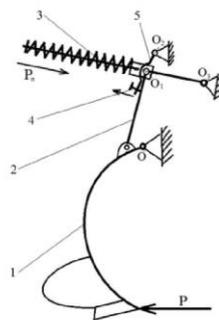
Схема запобіжного механізму фірми WHITE: 1 – стійка; 2 – важіль; 3 - пружина; 4 – упор; 5 – важіль.
